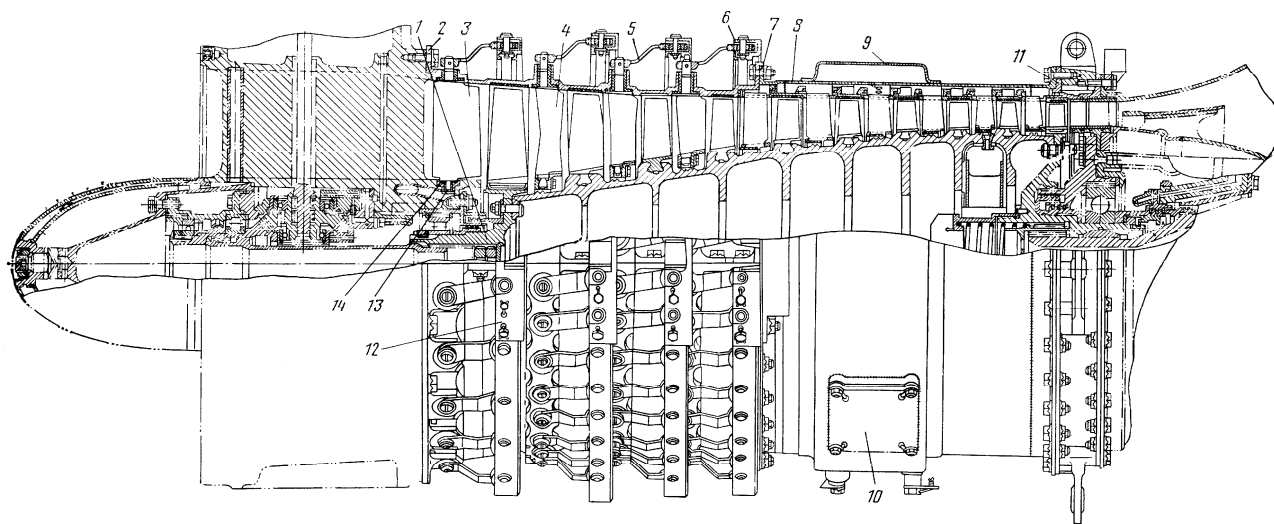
Компрессор двигателя (разрез верхней части):
